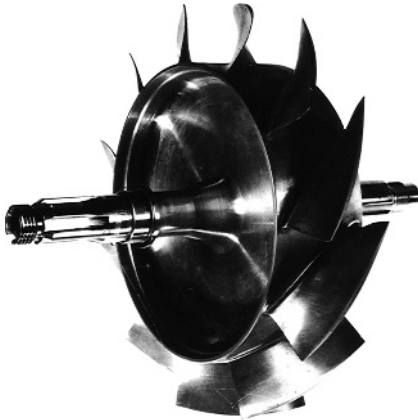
Axialverdichterrad, gefertigt aus einem Stück. Außendurchmesser 180 mm.
